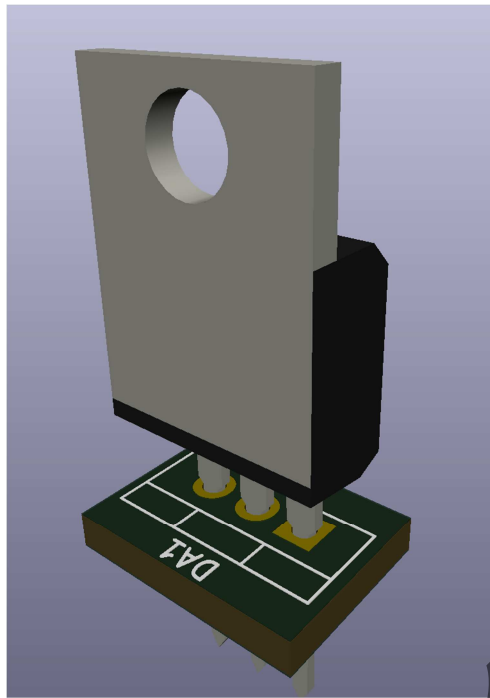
3D модель стабілізатора напруги LM 7805
